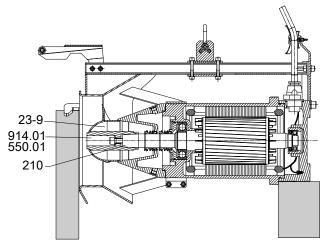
Montaje de la hélice axial; Amaline 300 con motor 8 6
